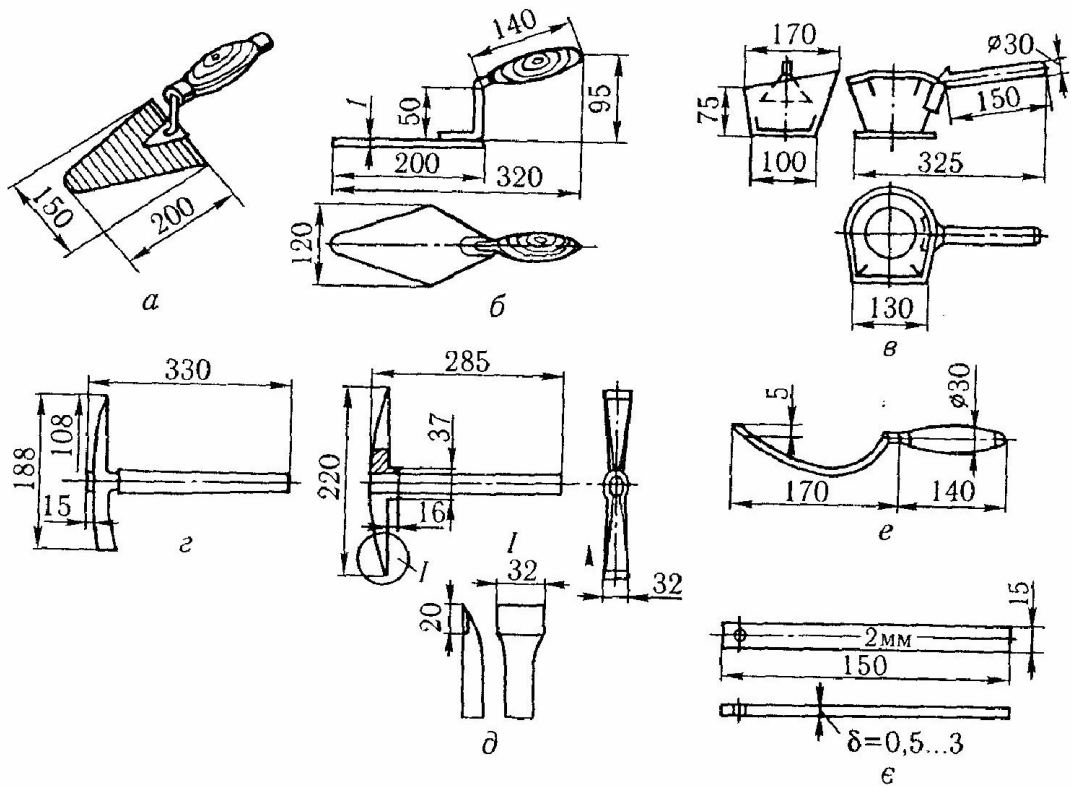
Типовий ручний інструмент: а - комбінована кельма; б - кельма для вогнетривника; в - ківш для вогнетривного розчину; г - молоток-кирка; д - кирка з лезом із твердого сплаву; е - розшивка; є - щуп робочий.
